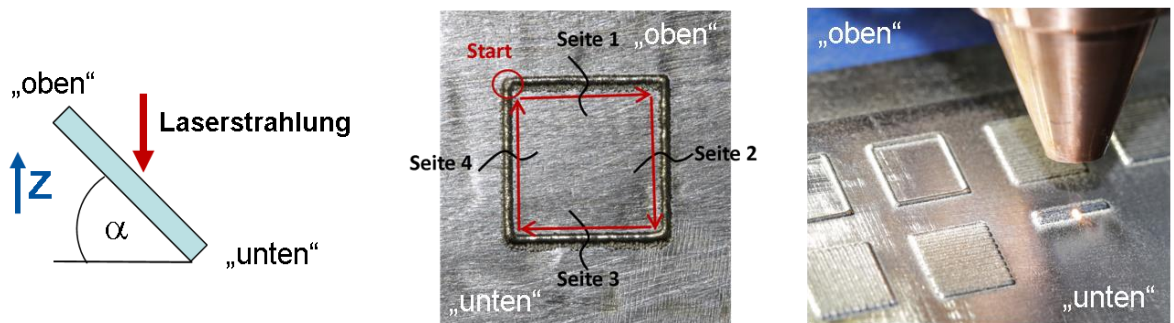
Auf geneigten Flächen (links) werden Quadrate (Mitte) und Flächen (rechts, Beispiel: Schweißen von oben nach unten) mittels LA auftragsgeschweißt
